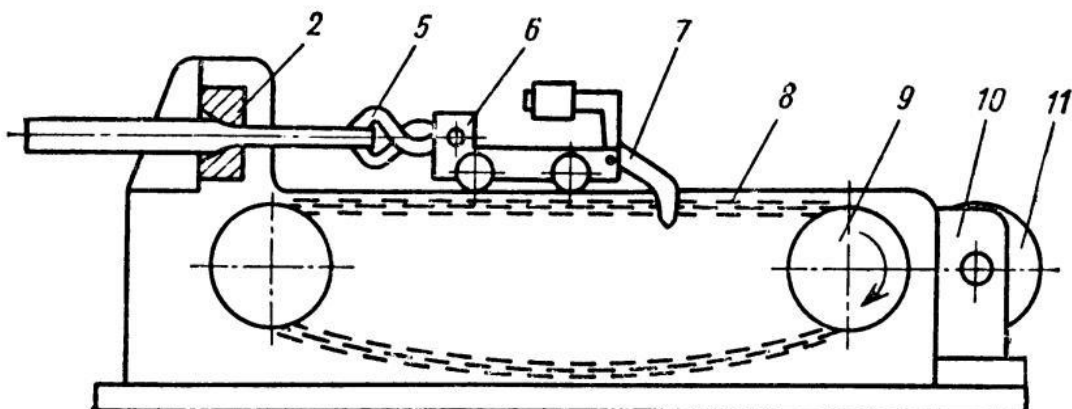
Принципиальная схема цепного волочильного стана. 2 – волока; 5 – клещи; 6 – каретка; 7 – тяговый крюк; 8 – пластинчатая цепь; 9 – звёздочка; 10 – редуктор; 11 – электромотор
